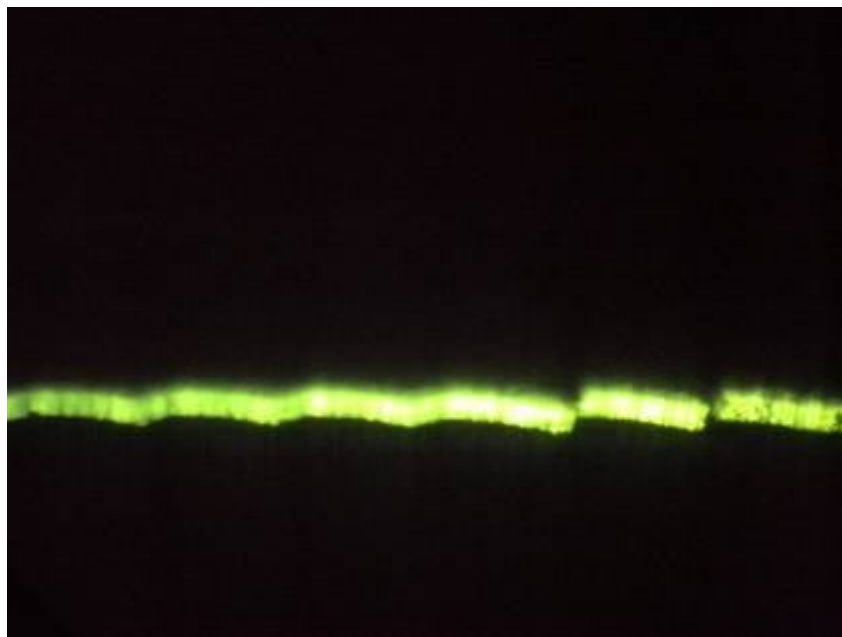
Шероховатость поверхности стали с применением СОЖ – Аквол-11 при чистовой обработке
